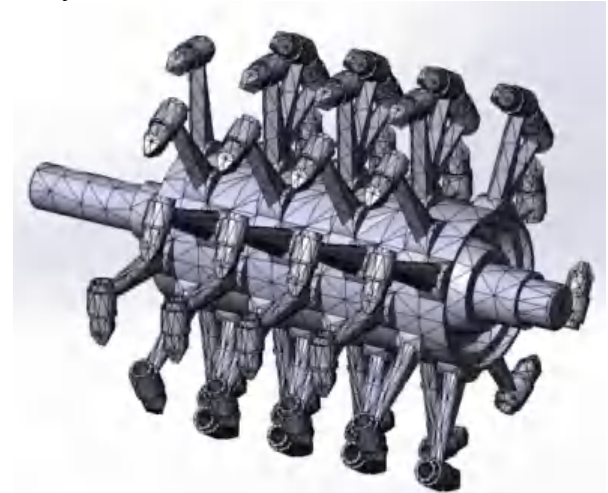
Загальний вигляд робочого органа для руйнування дорожніх покриттів.
